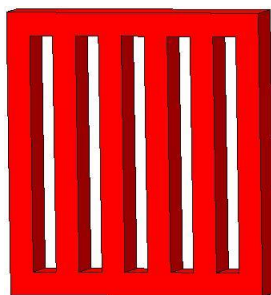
Бердо для станка, напечатанное на 3D-принтере.
